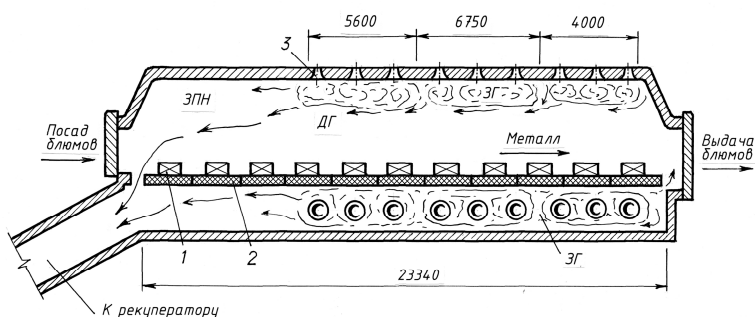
,а. Схема нагревательной печи стана 850 РУП «БМЗ»: 1 – заготовка; 2 – шагающие балки; ЗПН – зона предварительного нагрева; ДГ – дымовые газы
